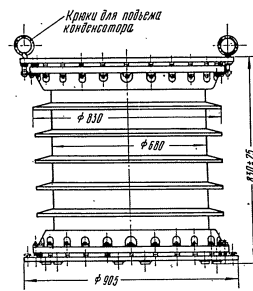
Габаритные размеры конденсатора типа ОМР 35-0,0535.
